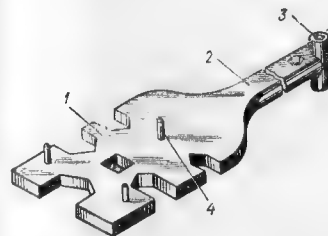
1 — корпус; 2 — ручка; 3 — головка торцовых ключей; 4 — штырь рожек ключа под гайки с отверстиями на торце
